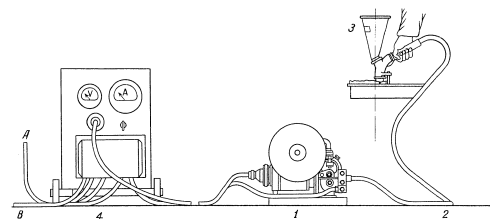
Схема шлангового полуавтомата ПШ-5:
